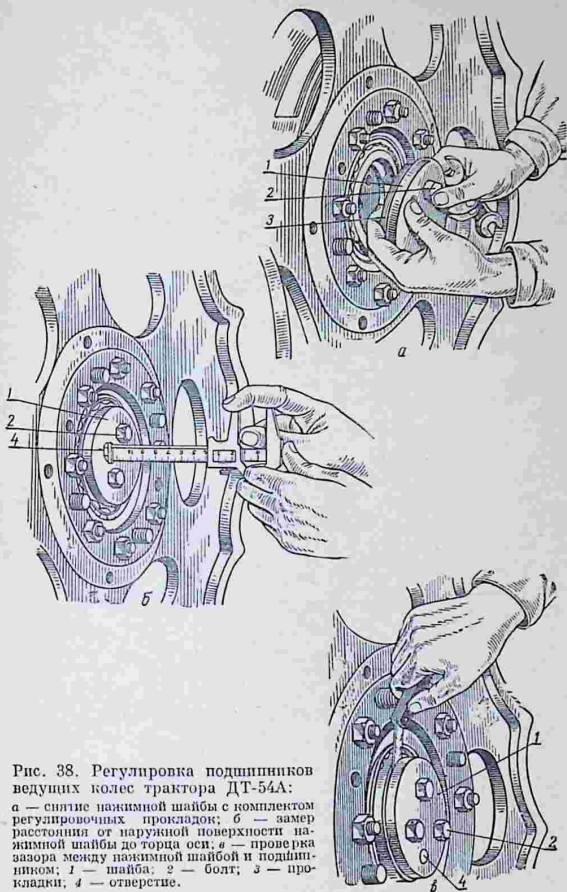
Регулировка подшипников ведущих колес трактора ДТ-54А:
